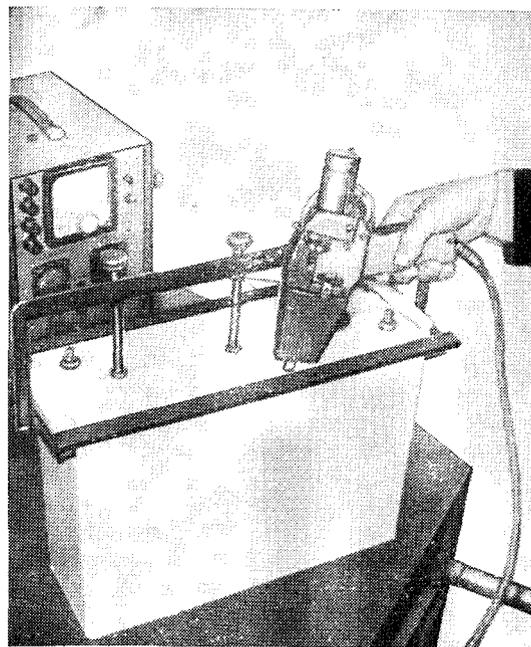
Приварка крышек конденсаторов в изоляционных корпусах на полуавтомате СА-124М
